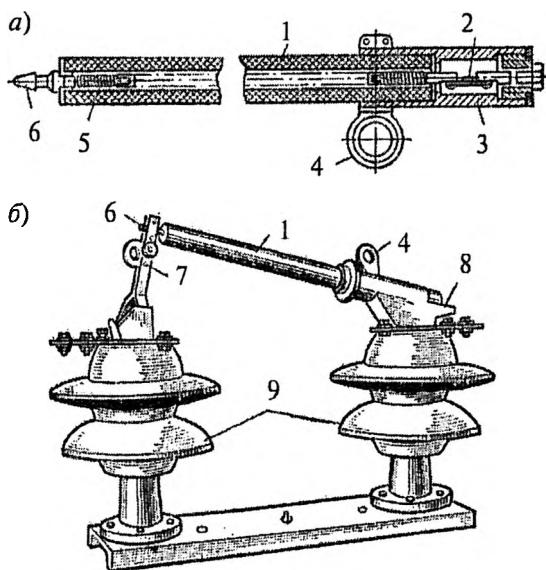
Плавкий предохранитель ПСН-35: а – разрез; б – внешний вид установки; 1 – трубка из газогенерирующего материала; 2 – плавкая вставка; 3 – металлический колпак; 4 – скоба; 5 – гибкий проводник; 6 – наконечник; 7 – рычаг; 8 – держатель; 9 – изоляторы
